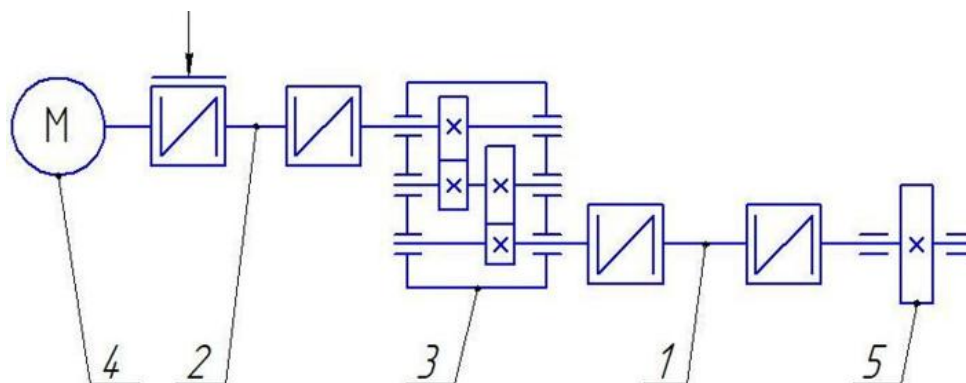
Кинематическая схема привода передвижения тележек до модернизации (КПД = 0,80):
